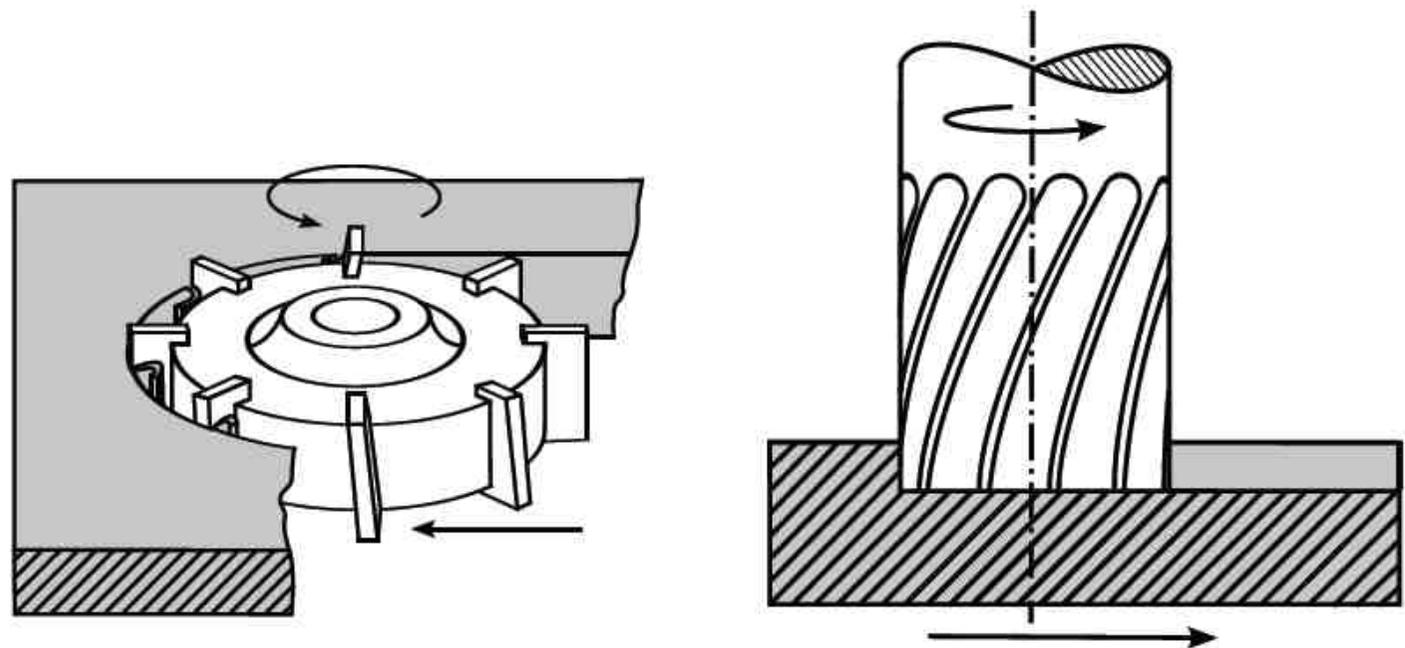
Fresamento frontal (esquerda). Fresamento frontal de canaletas com fresa de topo (direita).
